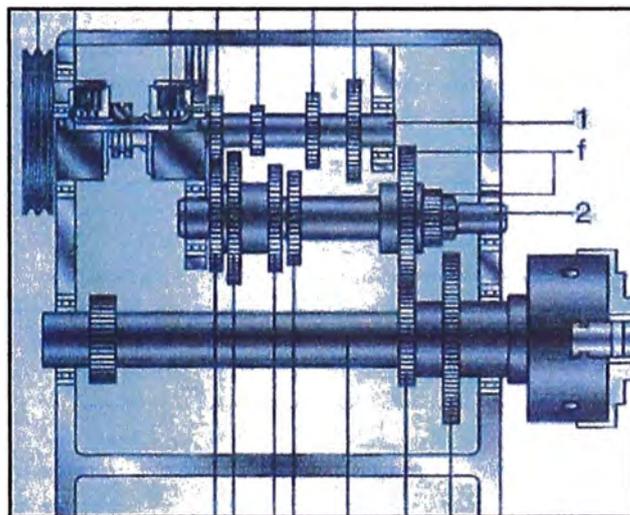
Cabezal Fijo con Engranajes
